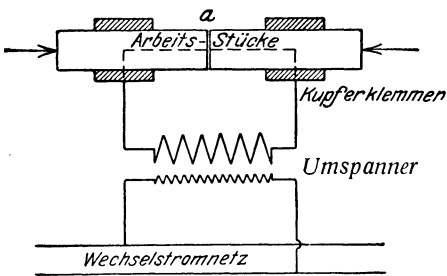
Grundform der elektrischen Stumpfschweißung.
